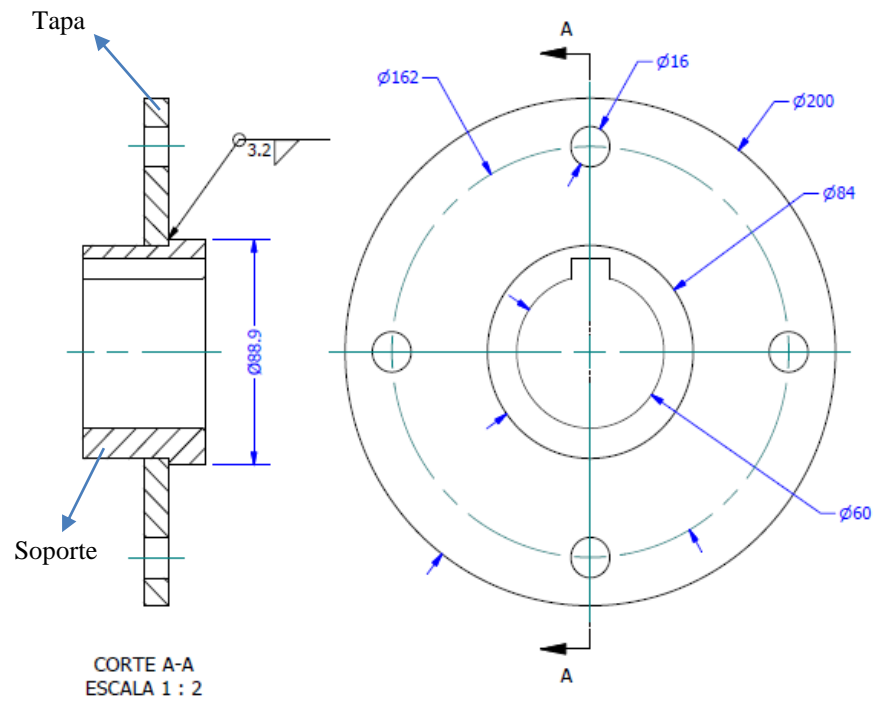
Dimensiones del conjunto tapa-soporte del rodillo
